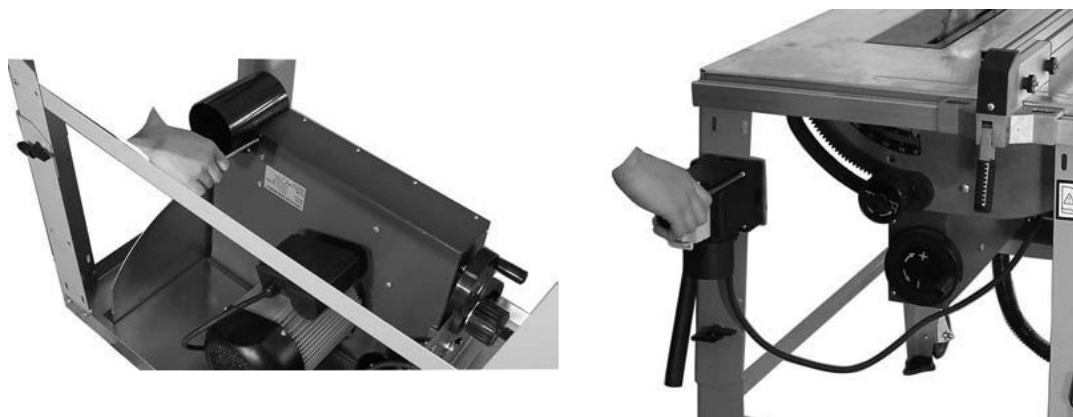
Bouche d'aspiration et montage de l'interrupteur
